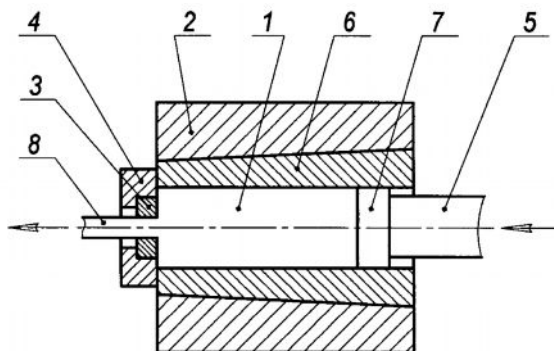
Схема процесса прессования: 1 - заготовка; 2 - контейнер; 3 - матрица; 4 - матрицедержатель; 5 - пуансон; 6 - втулка контейнера; 7 - пресс-шайба; 8 - пресс-изделие
